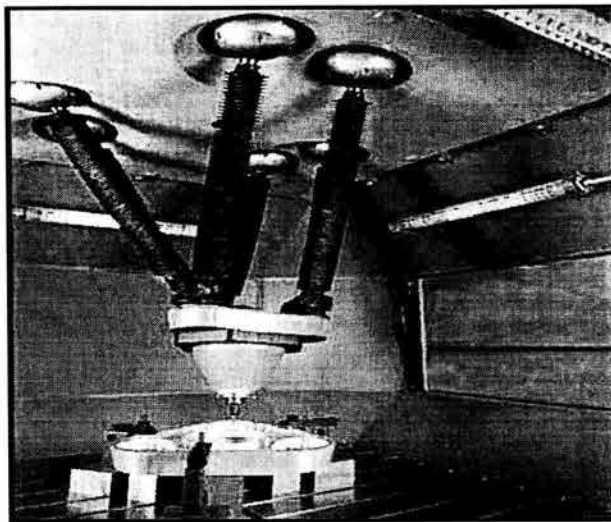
Robot Hexapod de juntas de bola en un centro de maquinado.
